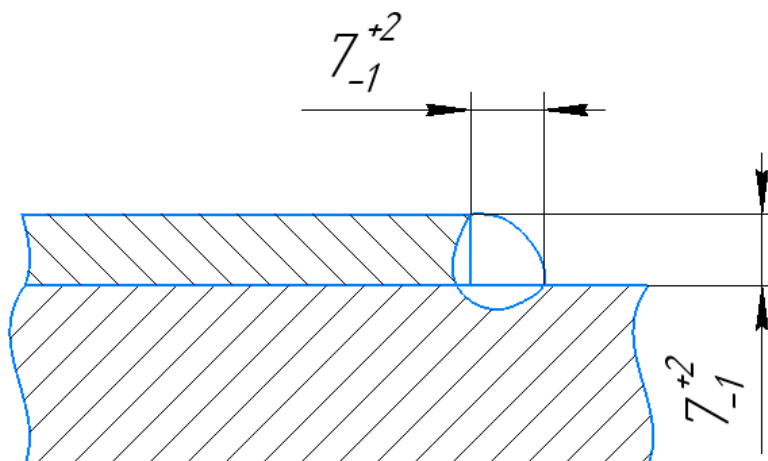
Геометрические размеры нахлесточного сварного соединения Н1 по ГОСТ 5264-80
